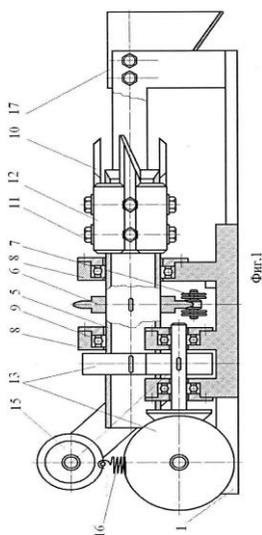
Устройство для заготовки хвойной лапки (вид сбоку)
